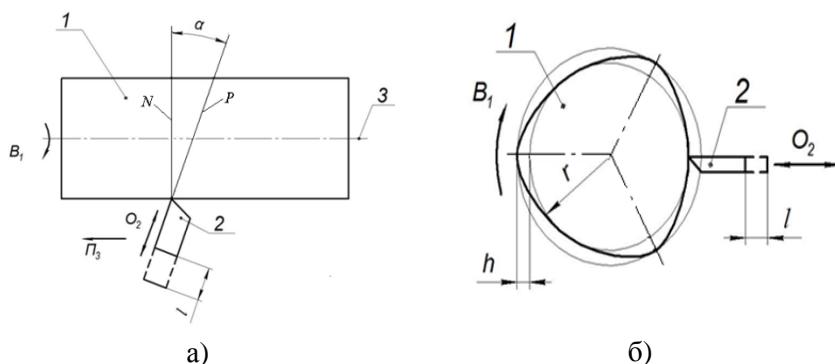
Кинематическая схема обработки (а) и схема профилирования (б) некруглой поверхности
